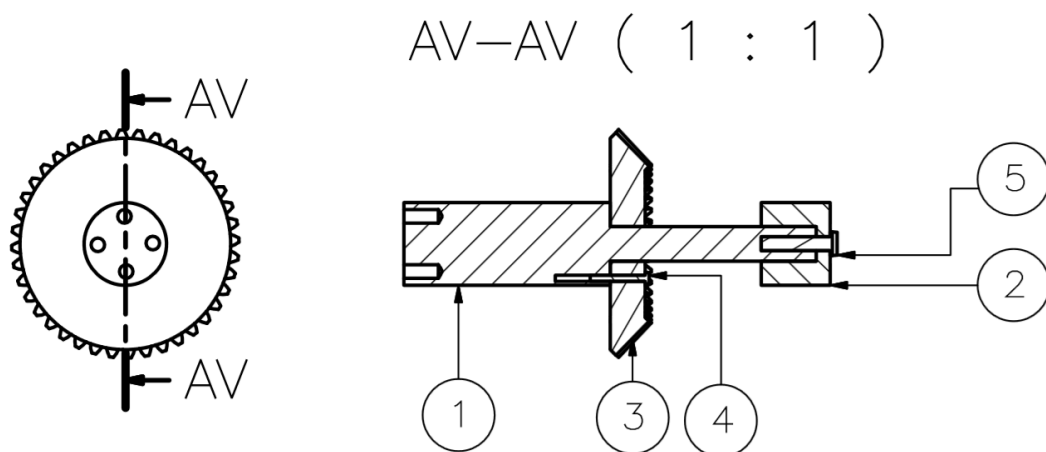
Corte AV de ensamble de acoplamiento de Gripper
